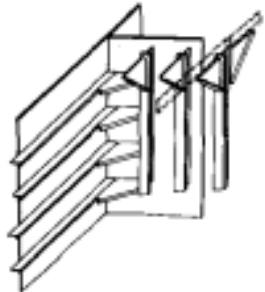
Крепление к стойкам поперечной переборки приваленного набора бортов
